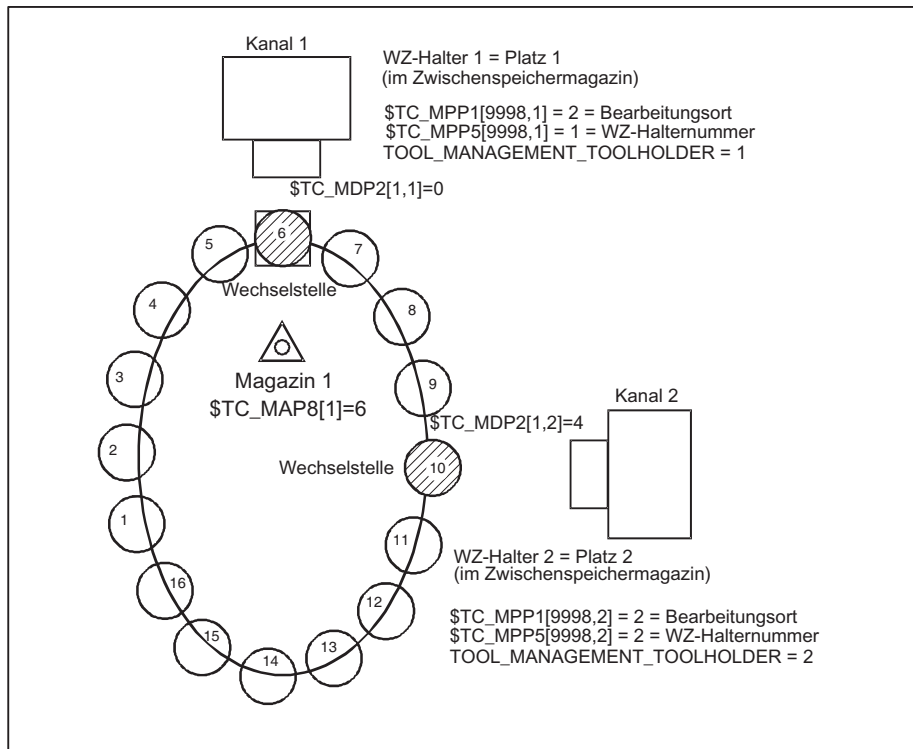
2 Kanäle mit je einem Werkzeughalter und einer TO-Einheit
